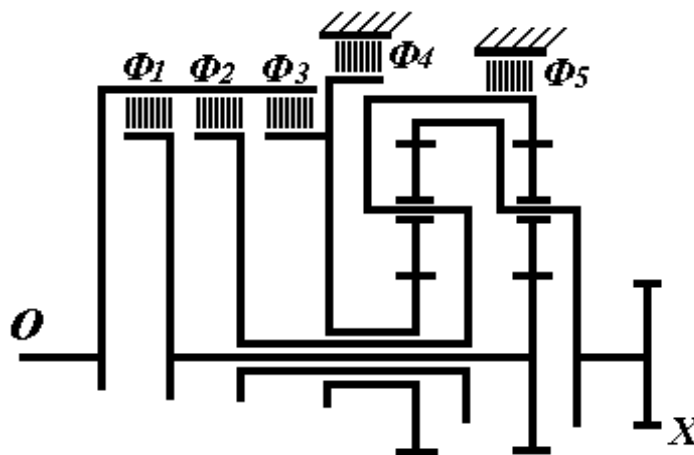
Схема четырехступенчатой коробки передач
